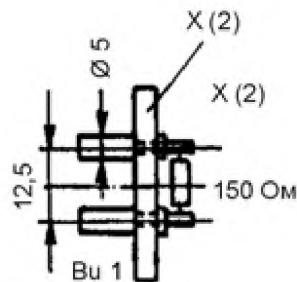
Дополнительные конструктивные детали открытой полосковой ТЕМ-камеры
